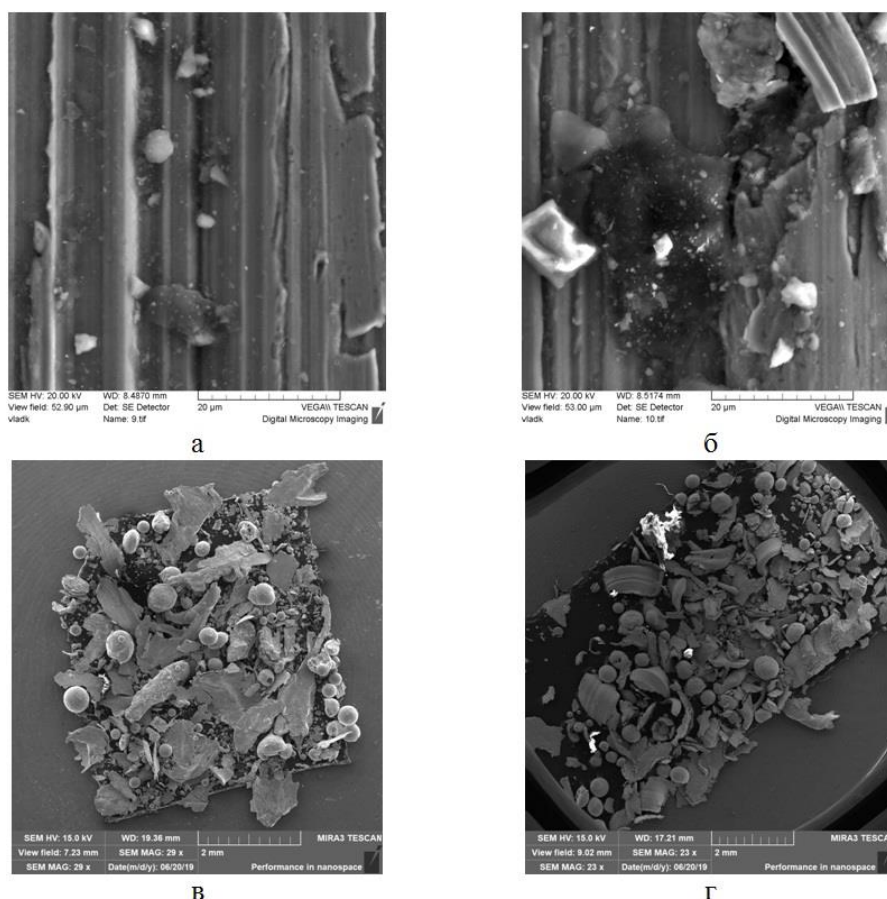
Морфология поверхностей заготовки после резания абразивным и алмазными кругами (а, в – абразивный круг, б, г - алмазный)
